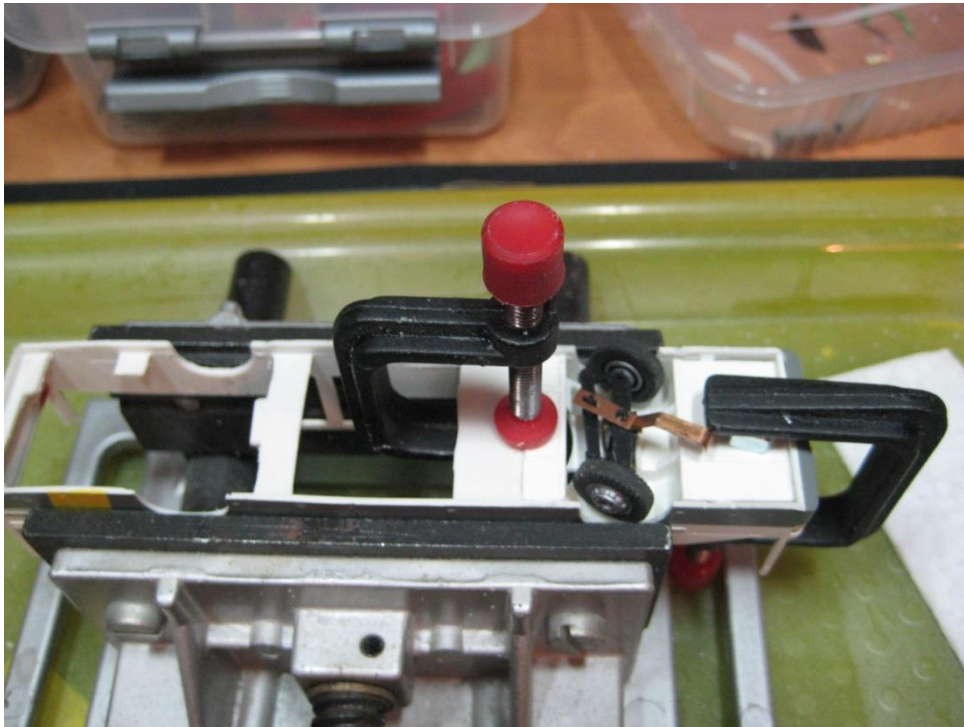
voorste bodemplaat op zijn plaats lijmen.
